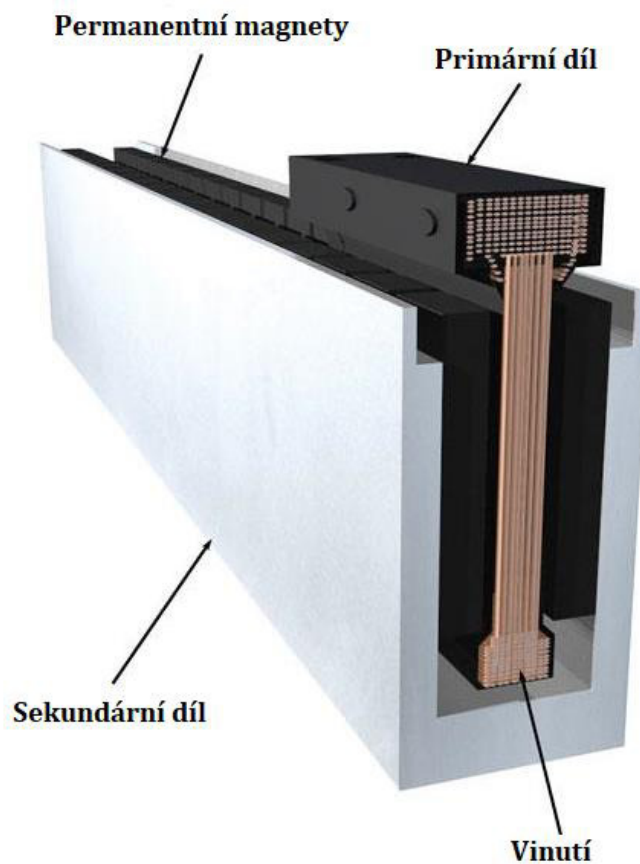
Lineární motor se železným jádrem, modifikováno z [7]
